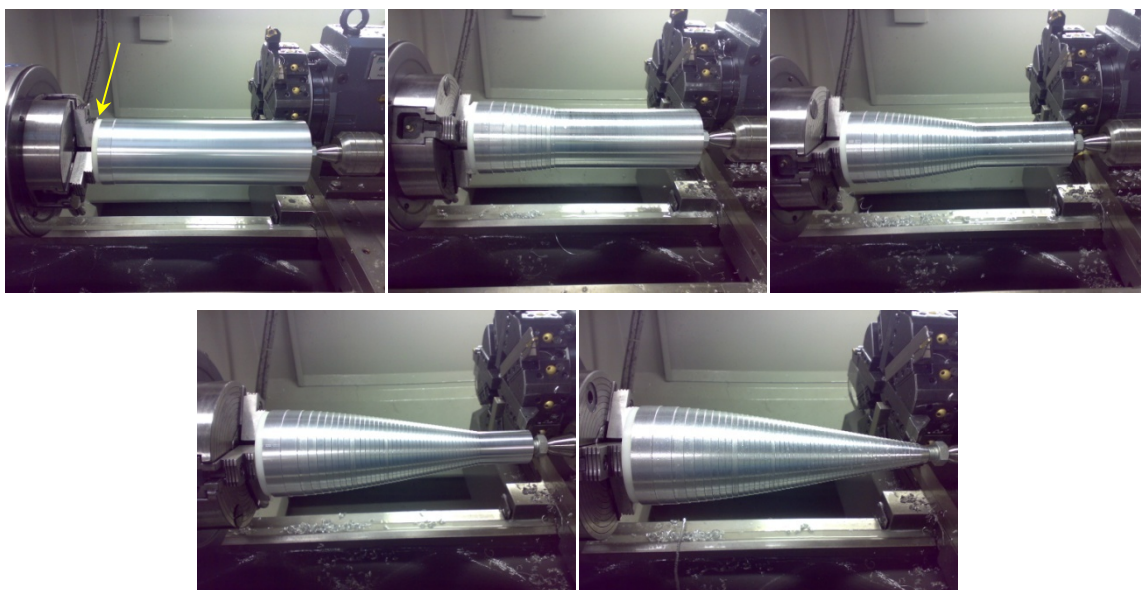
Processo de usinagem da cauda no torno CNC
